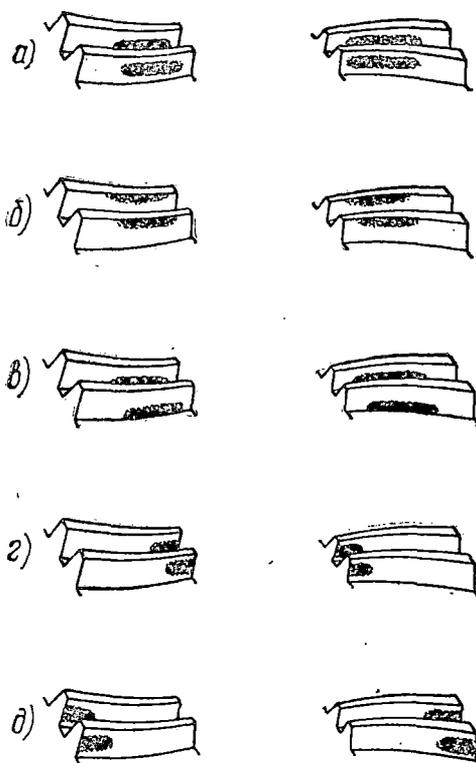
Пятна контакта на зубьях шестерен главной передачи:
